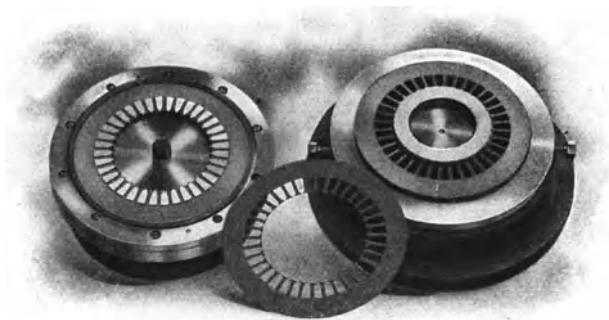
Ansicht des Werkzeuges in Abb. 208—9.
